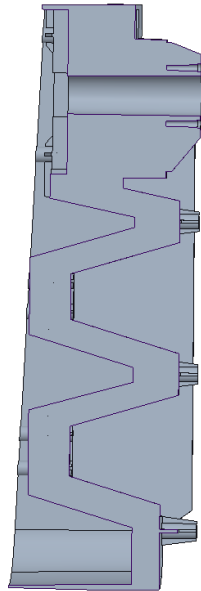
Corte de columna media con diseño horizontal.
